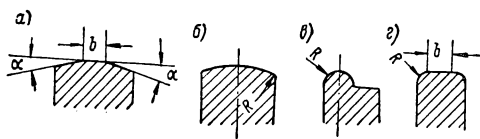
Формы рабочего профиля роликов для обкатывания поверхностей.
